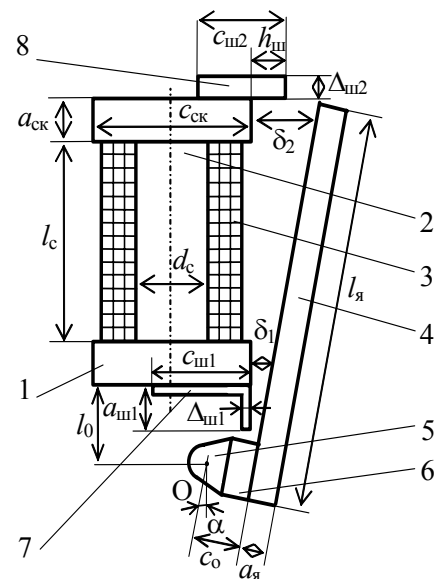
Эскиз электромагнита с поперечным движением якоря с ферромагнитными шунтами в рабочих зазорах для контактора переменного тока
